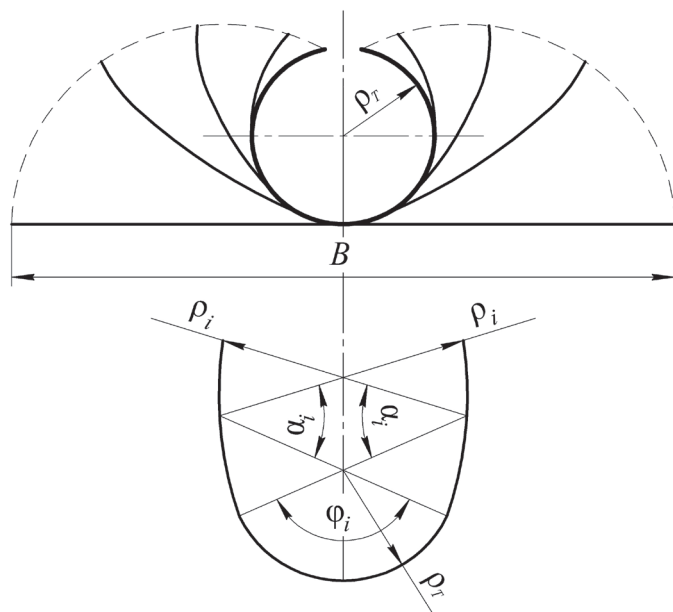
«Цветок» формовки и профиль i -го калибра для двухрадиусной калибровки с изгибом центрального участка
